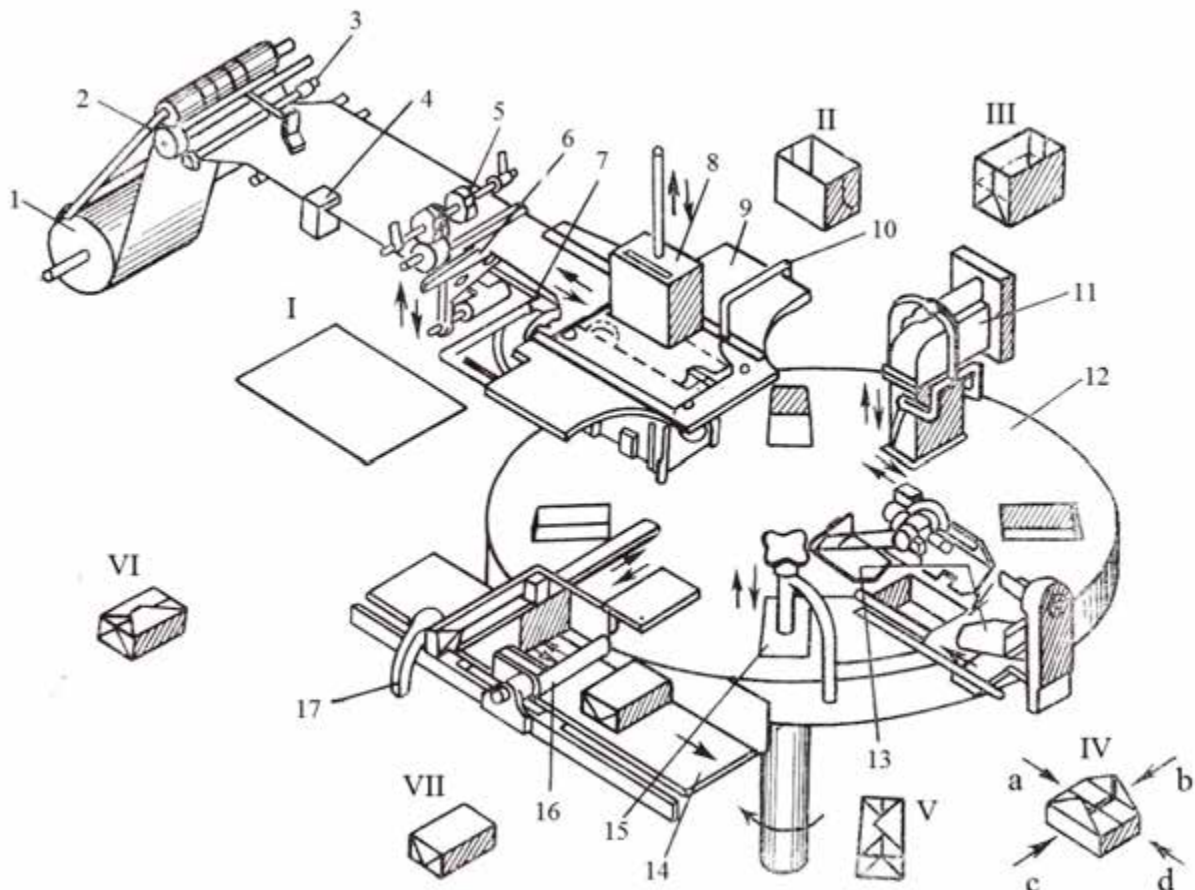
Технологічна схема автомата М6-АР1М: 1 – бобіна з пакувальним матеріалом; 2 – притиск, 3 – валик; 4 – пристрій для нанесення дати; 5 – протяжні роликки; 6 – ножі; 7 – захвати, 8 – пуансон; 9 – матриця; 10 – щуп; 11 – дозатор; 12 – формувальний стіл; 13 – механізм загортання пакета; 14 – відвідний транспортер; 15 – механізм ущільнення; 16 – перегортач коробок; 17 – знімач
